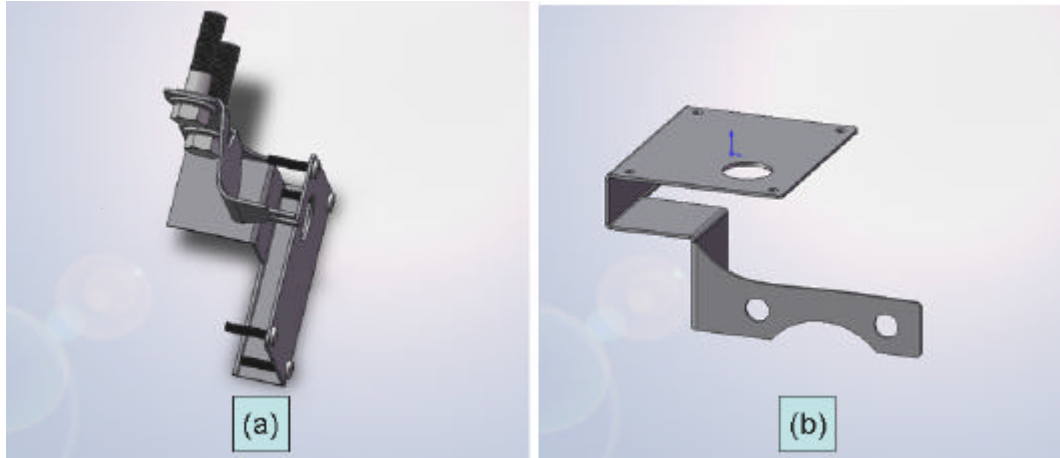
(a) Desain Chasing Bottom Side (b) Desain Chasing Up Side
